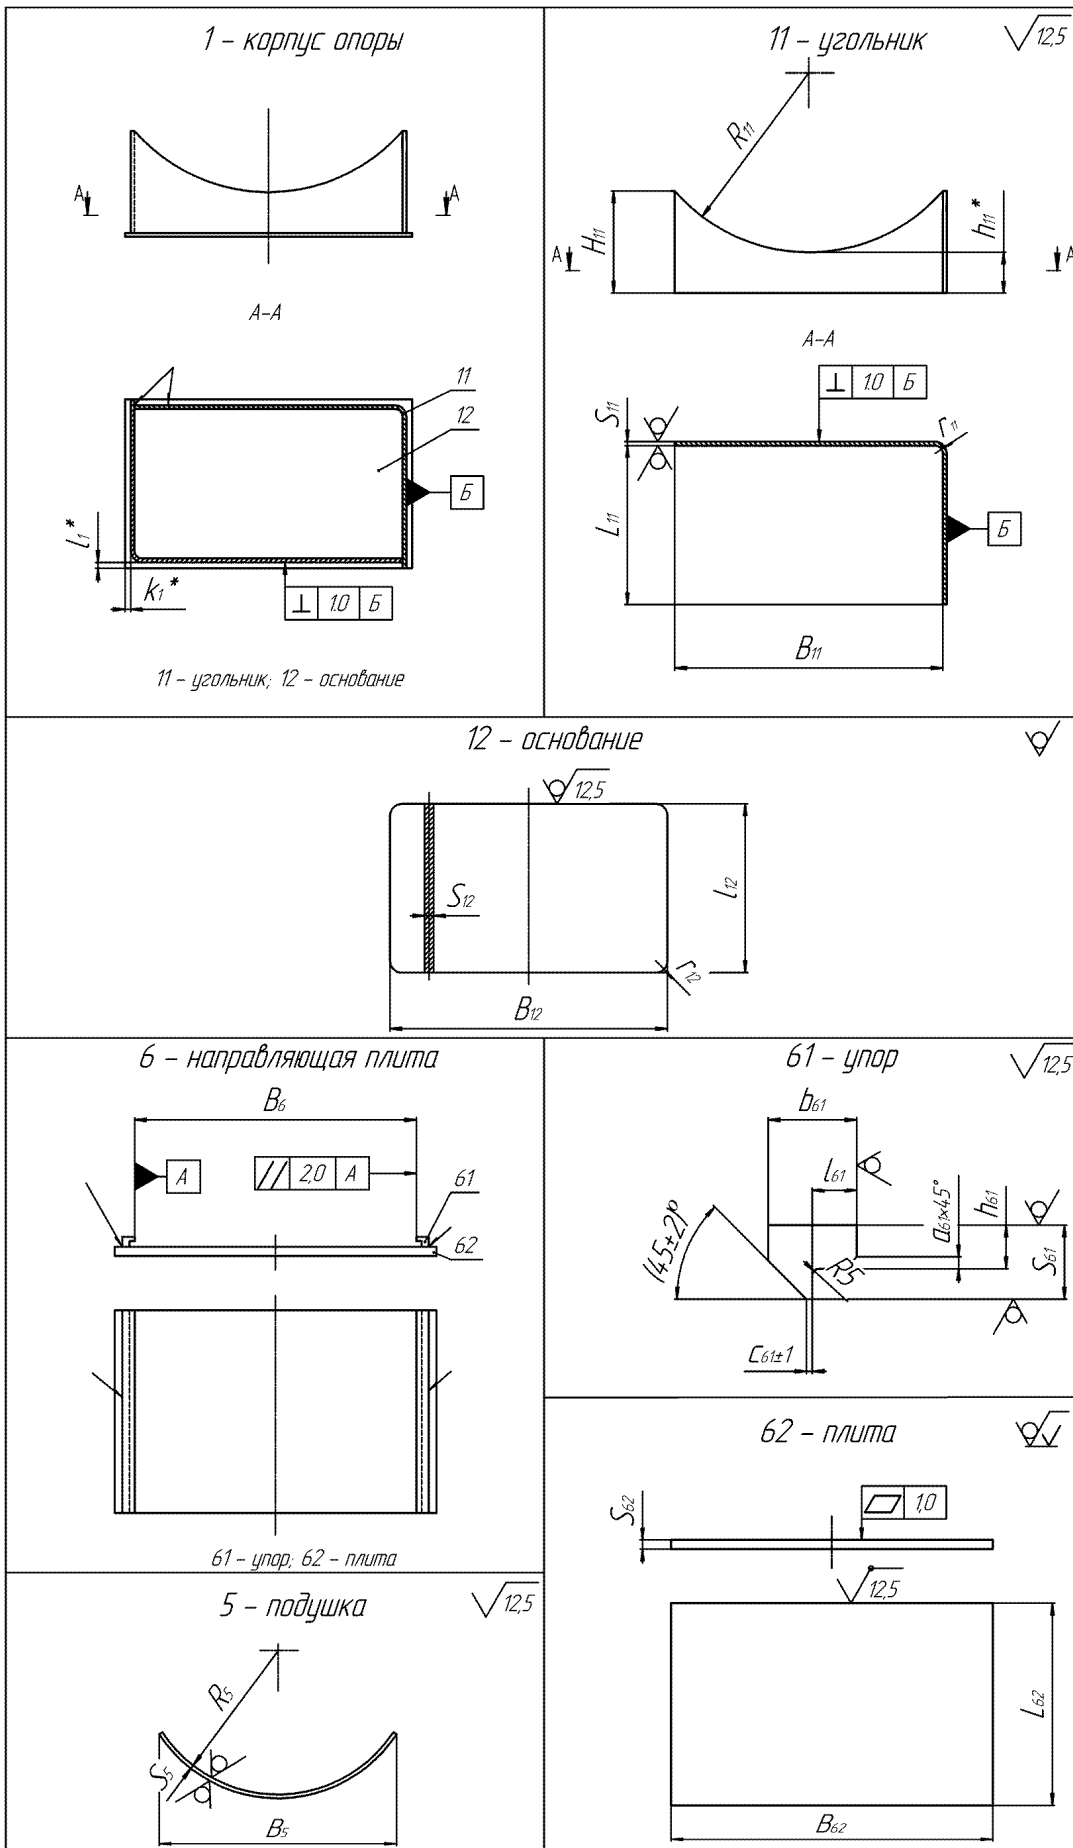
Детали изделий 02-XXXX-G-1C-XX-A,
